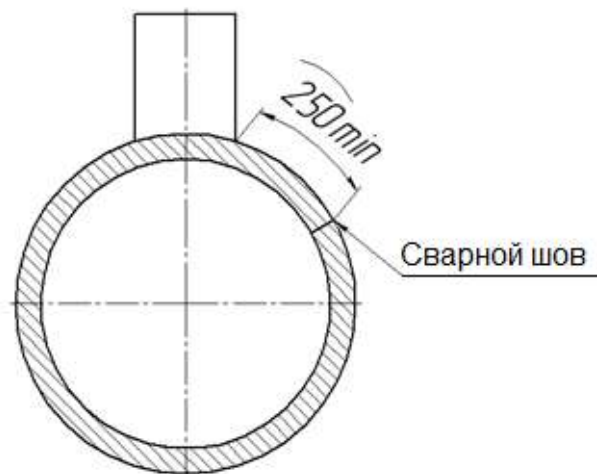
Расположение штуцера (тройникового соединения, прямой врезки, патрубка, бобышки) в зависимости от расположения продольного сварного шва основной трубы
